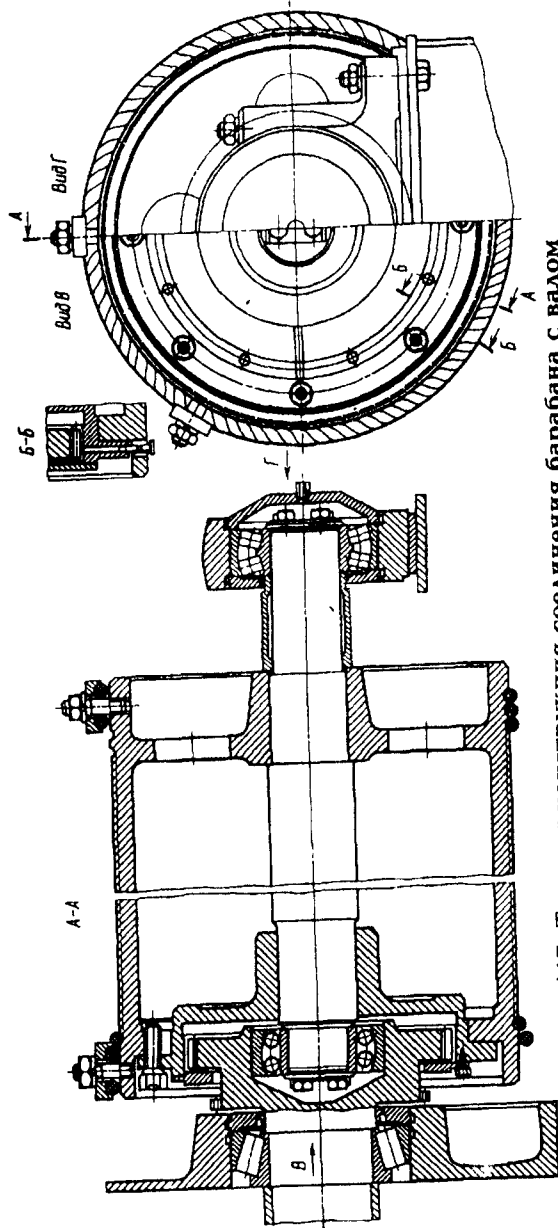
Типовая конструкция соединения барабана с валом редуктора с помощью зубчатой муфты
